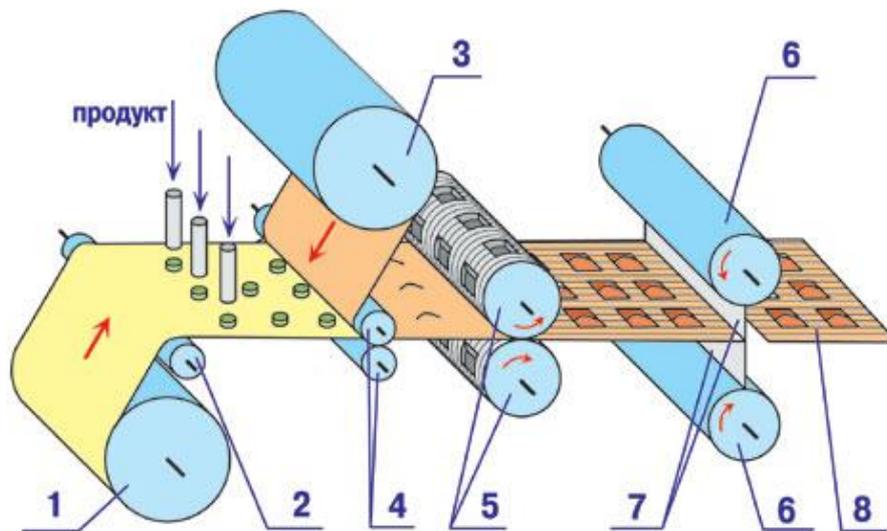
Схема упаковочной машины горизонтального типа непрерывного действия, образующей плоский пакет наложением полос с двух рулонов: 1 - нижний рулон; 2 - ролик; 3 - верхний рулон; 4 - ролики; 5 - ротора сварочные; 6 - ротора отрезки; 7 - ножи; 8 - готовый пакет
